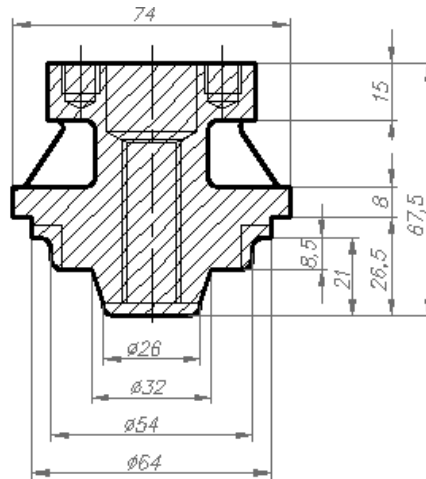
Ескіз заготовки для литва в кокіль
